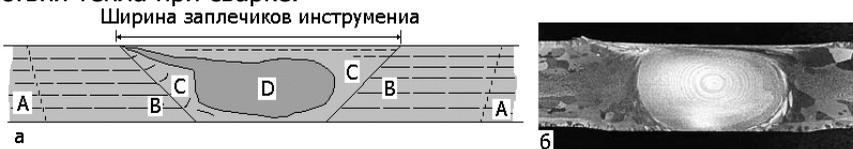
Схема строения поперечного сечения сварного соединения.
